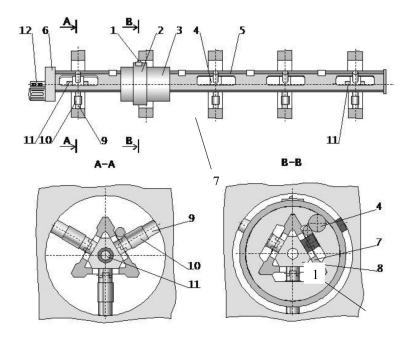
Компоновочная схема портативного станочного модуля для расточной обработки поверхностей отверстий постелей вкладышей коренных подшипников коленчатого вала дизеля 1А5Д49: 1 — резец; 2 — вращающееся кольцо; 3 — корпус расточной головки; 4 — шестерня; 5 — приводной вал; 6 — редуктор; 7 — опорная штанга; 8 — упорный механизм; 9 — упорные лапки; 10 — регулировочный механизм; 11 — фотоприемное устройство; 12 — лазерный излучатель
